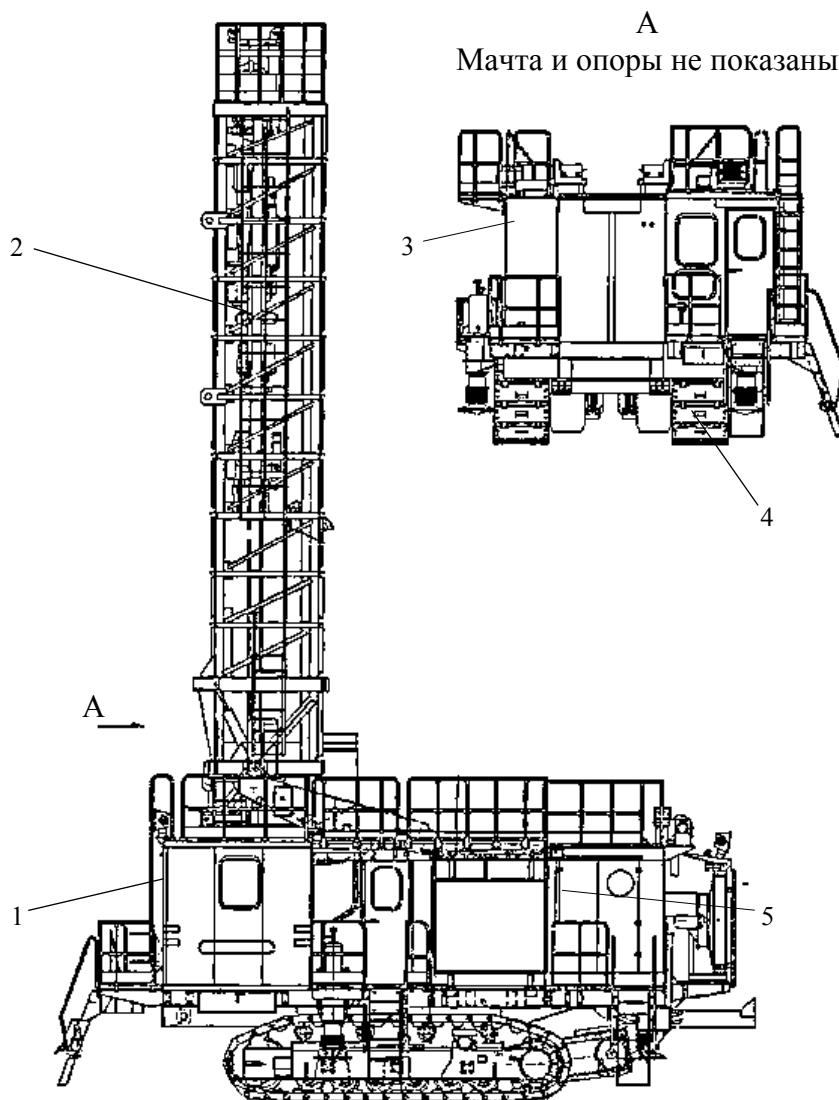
Станок шарошечного бурения СБШ-250МНА-32
